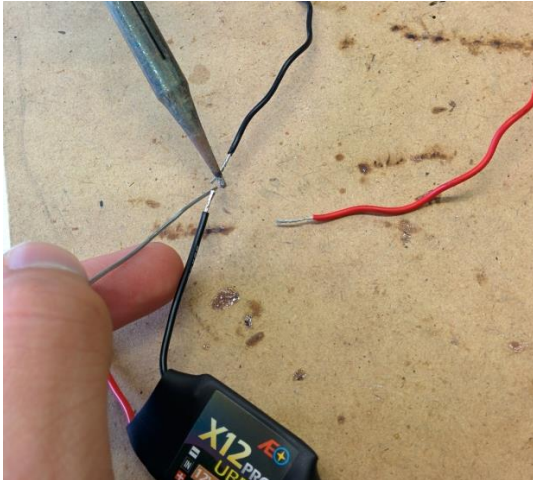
Soldant els cables d'alimentació al BEC.
